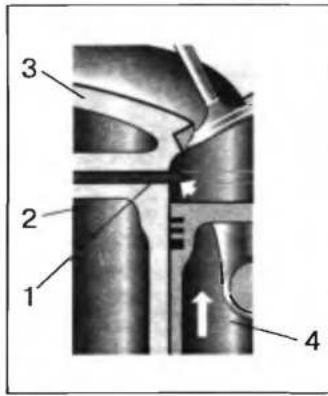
"Свисание" окантовки прокладки в цилиндр вызывает удар поршня в край окантовки в ВМТ, стук двигателя и быстрое прогорание прокладки. 1 — прокладка; 2 — блок цилиндров; 3 — головка блока; 4 — поршень; стрелкой указано место удара поршня по прокладке
